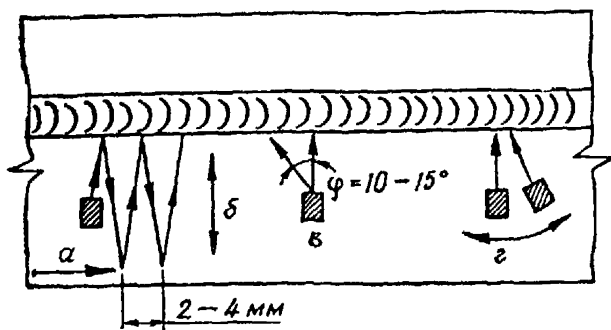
Схемы перемещения искательной головки при контроле сварного шва:
